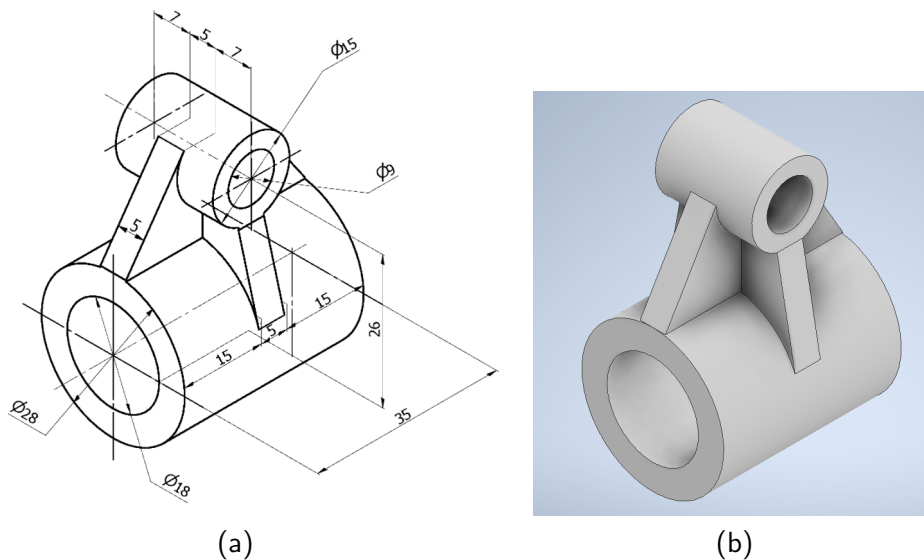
Vista isométrica de la pieza a dibujar con dimensiones en milímetros, (a) diseño base en milímetros, (b) diseño modificado.
